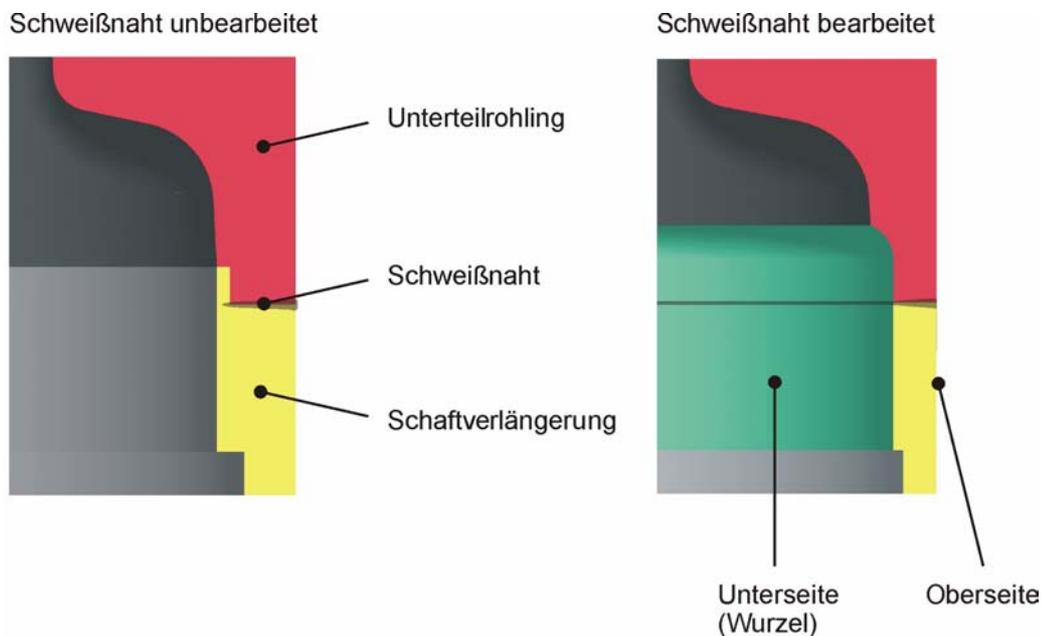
Bearbeiten der Schweißnaht
